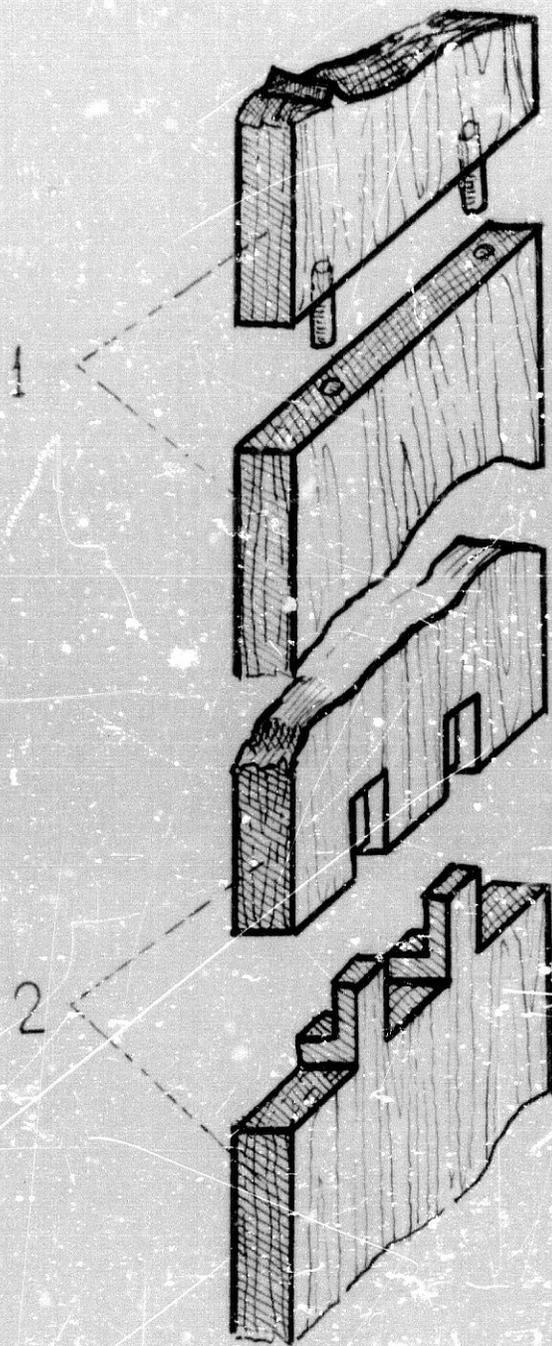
1) Ensamble empernado. 2) Ensamble de cola de milano en forma de lenguetas.
